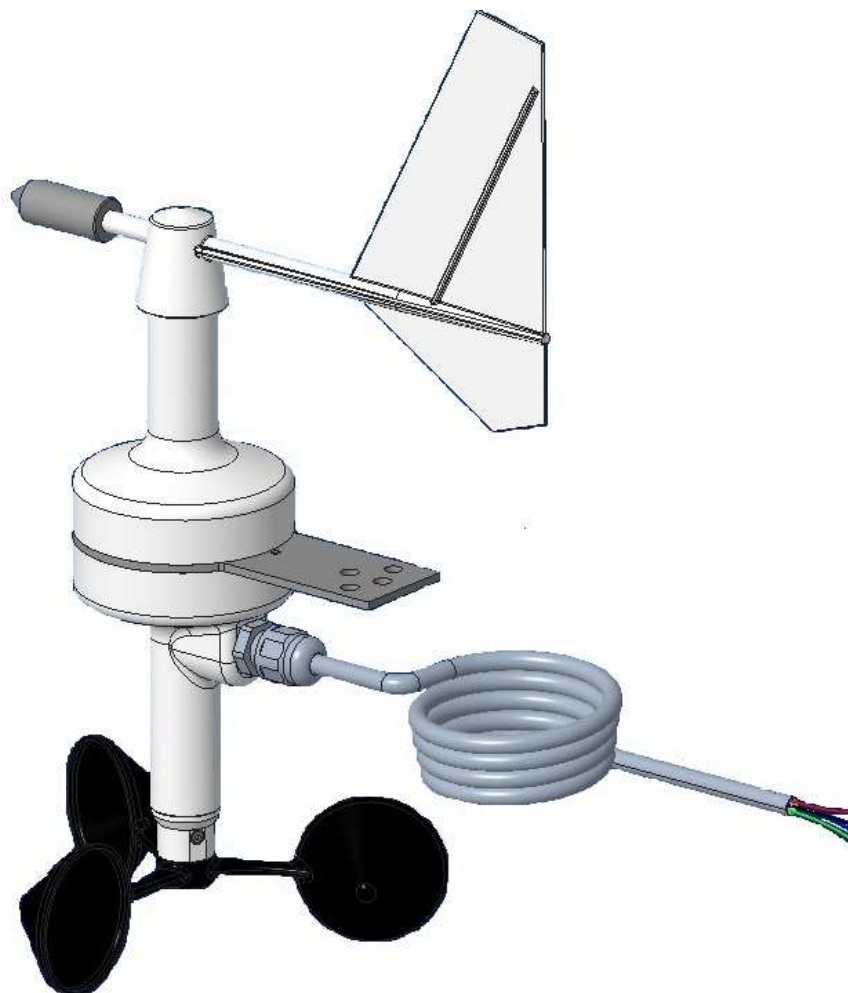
Внешний вид датчика ДСНВ ИСАТ.416136.005
